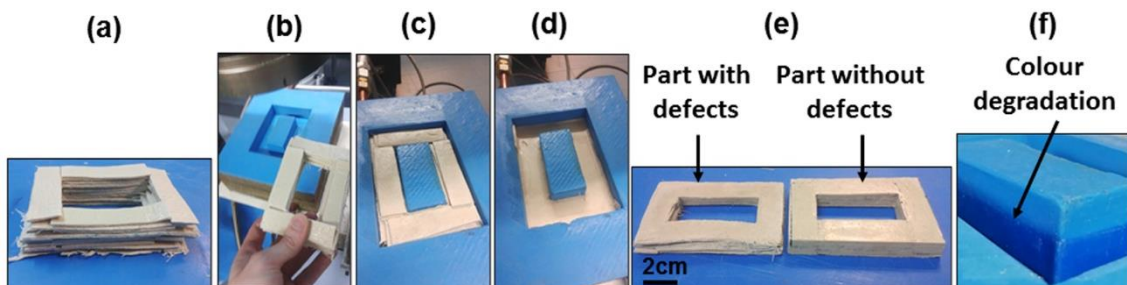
Pruebas de moldeo. (a) Apilamiento del preimpregnado. (b) Introducción manual del apilamiento. (c) Apilamiento antes del moldeo. (d) Apilamiento después del moldeo. (e) Piezas moldeadas. (f) Degradación del color de la funda de silicona.
